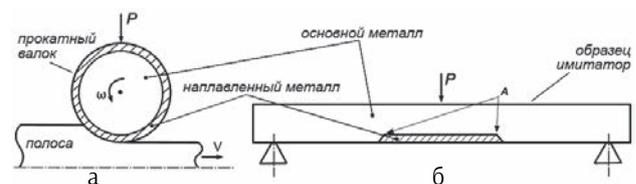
Схема прокатки полосы (а) и нагружение образца-имитатора по схеме трехточечного изгиба (б). Стрелками (А) указаны места перехода от основного металла к наплавленному металлу
